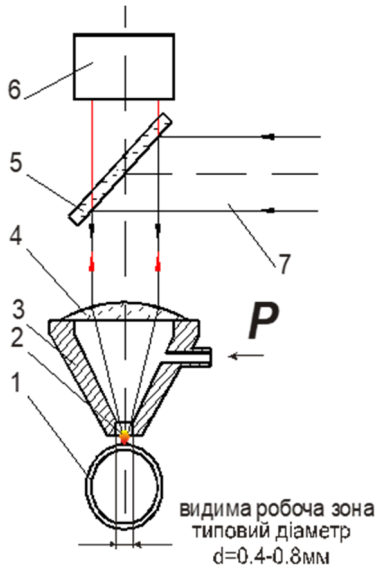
Схема процесу лазерного різання тонкостінної трубчастої заготовки з використанням конічного сопла: 1 – заготовка, 2 – плазмова хмара, 3 – конічне сопло для подачі робочого газу, 4 – об’єктив, що фокусує, 5 – поворотне дзеркало, 6 – телевізійна камера, 7 – лазерне випромінювання
